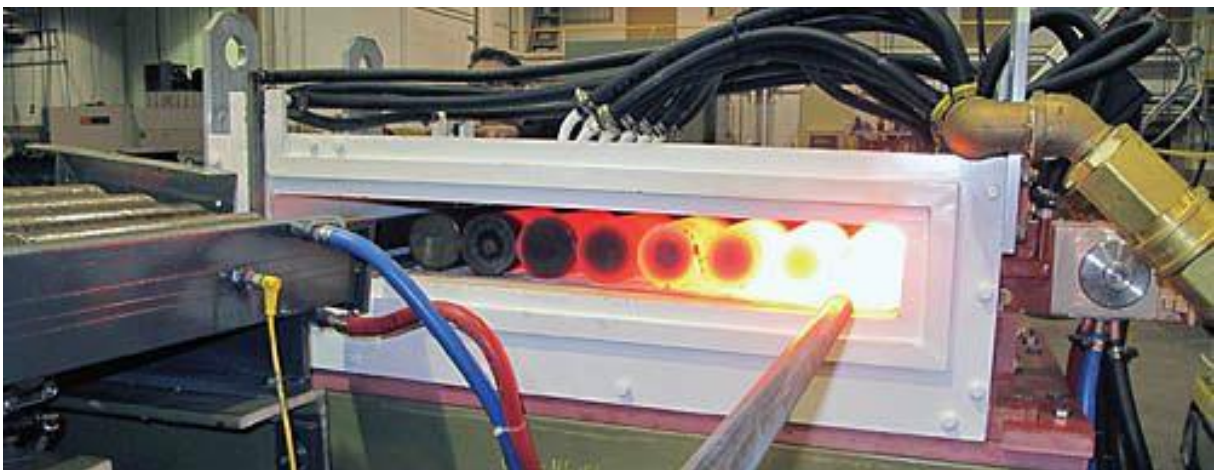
Příklad průběžného indukčního ohřevu tyčí [9]
